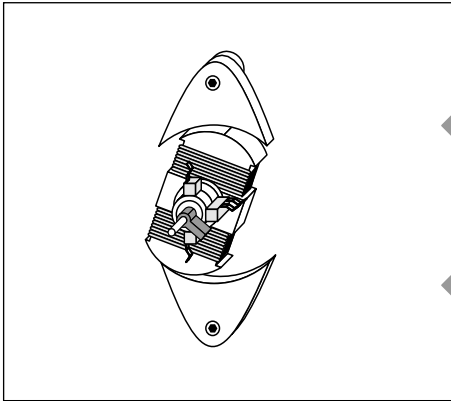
Sicherung des Rotors durch Bürstenbrücke
